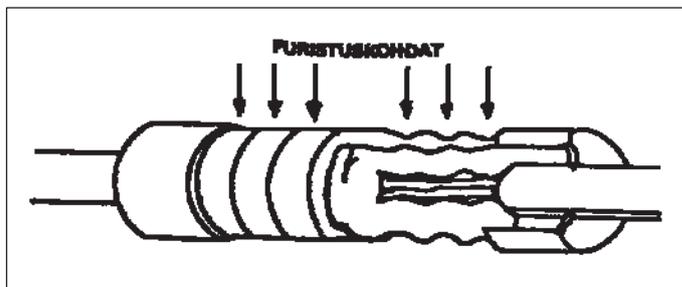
Конструкция изолированного контактного зажима и места опрессовки
